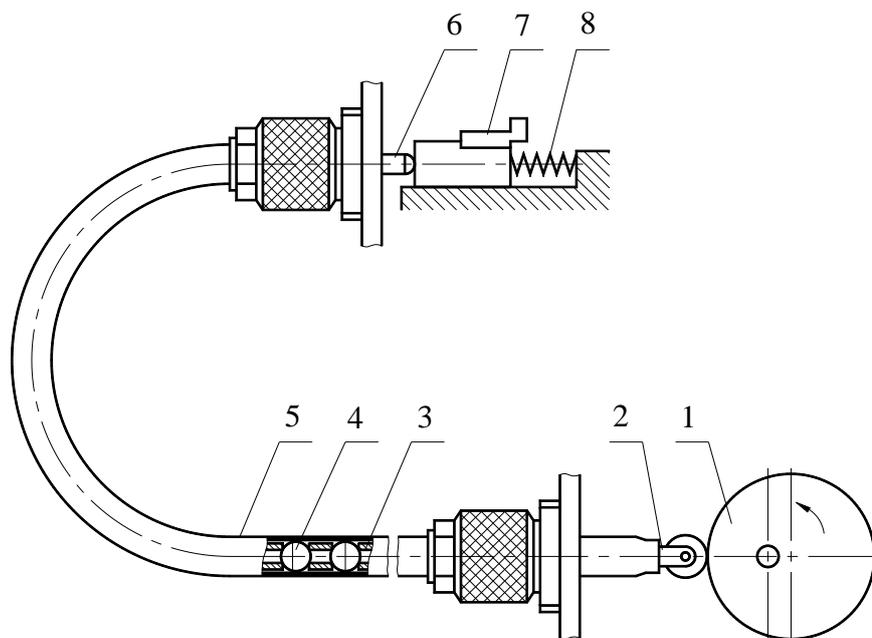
Схема шарикового передаточного механизма (ШПМ)
